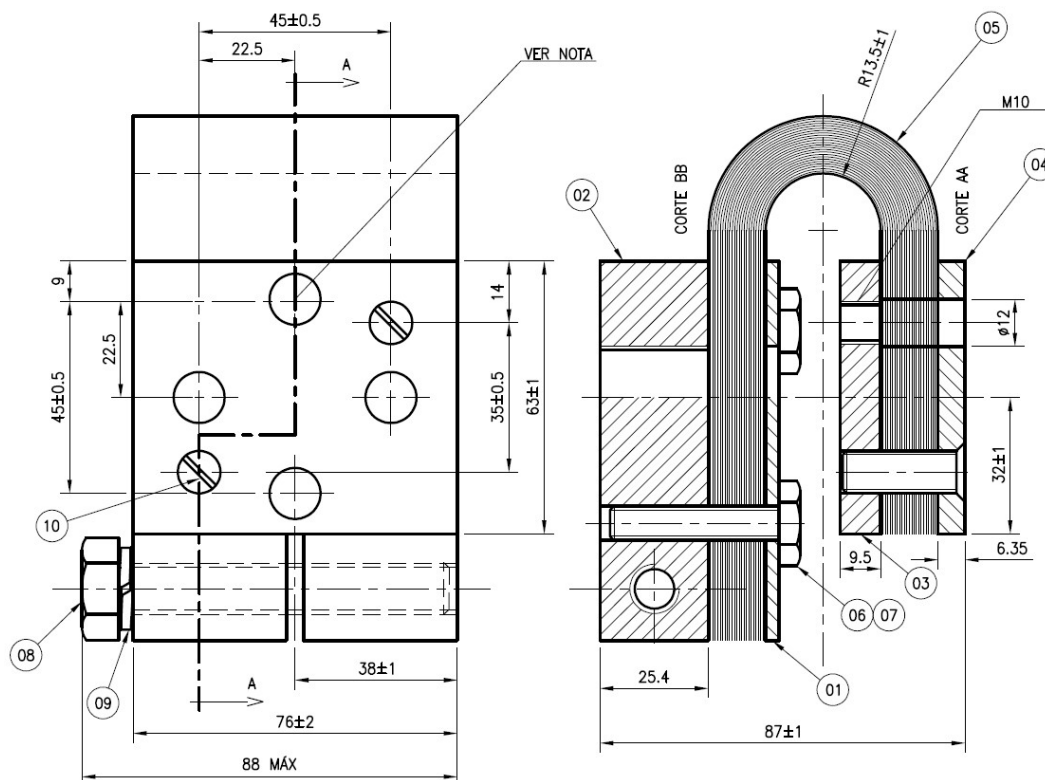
Dimensões para fixação do protetor de rede (1600A, 1875A e 2250A) ao transformador
